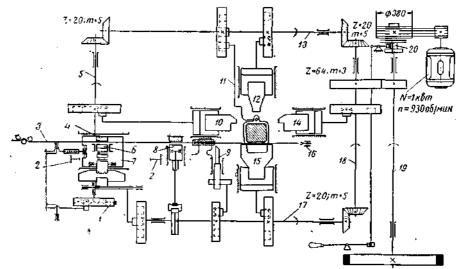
Кинематическая схема универсально-гибочного пресса-автомата модели A912Г
